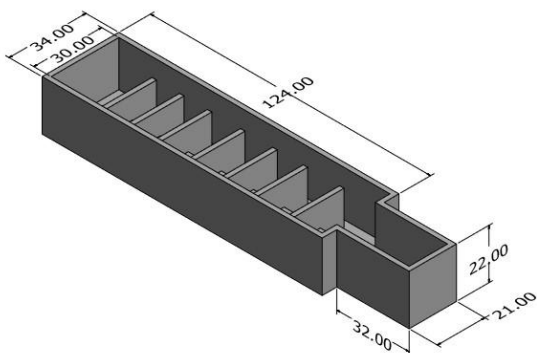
Dimensiones del molde superior. Vista isométrica. Medidas dadas en milímetros (mm).
